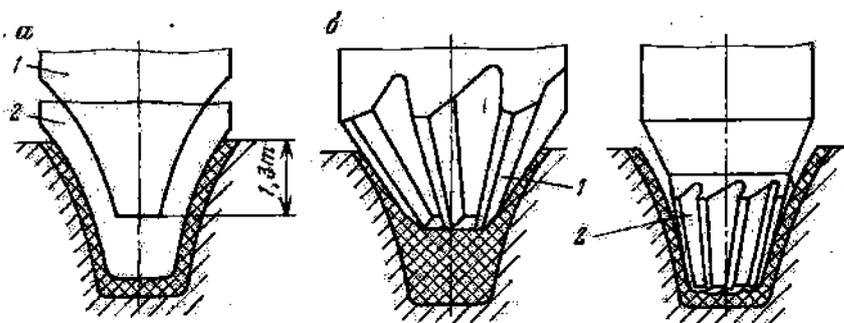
Схема чернового нарезания крупномодульных колес пальцевыми фрезами:
